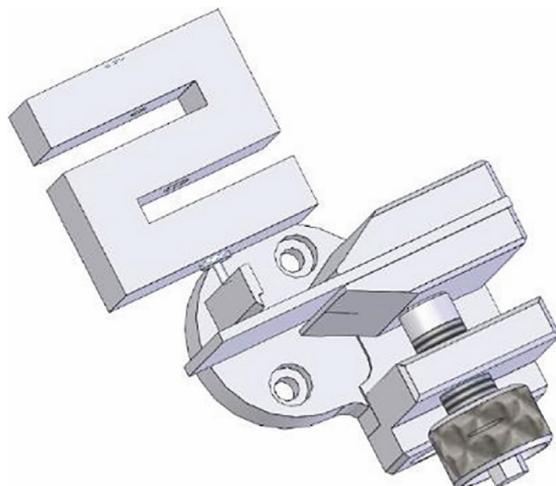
3-D-Zeichnung der Einspannbacken mit Probe, Kraftmesszelle und Stab
